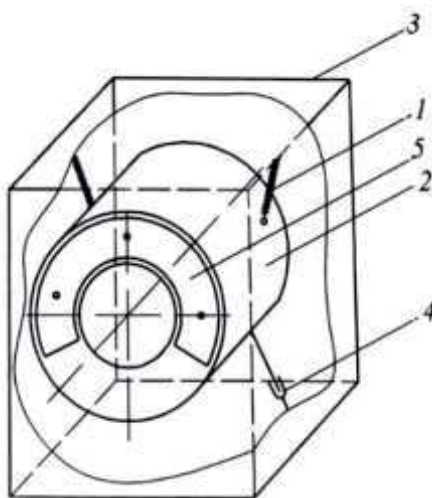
Загальна схема механізму віброгасіння коливань машин типу ПМА: 1 - пружина; 2 - бак; 3 - корпус; 4 - амортизуючі пристрої; 5 – противаги
